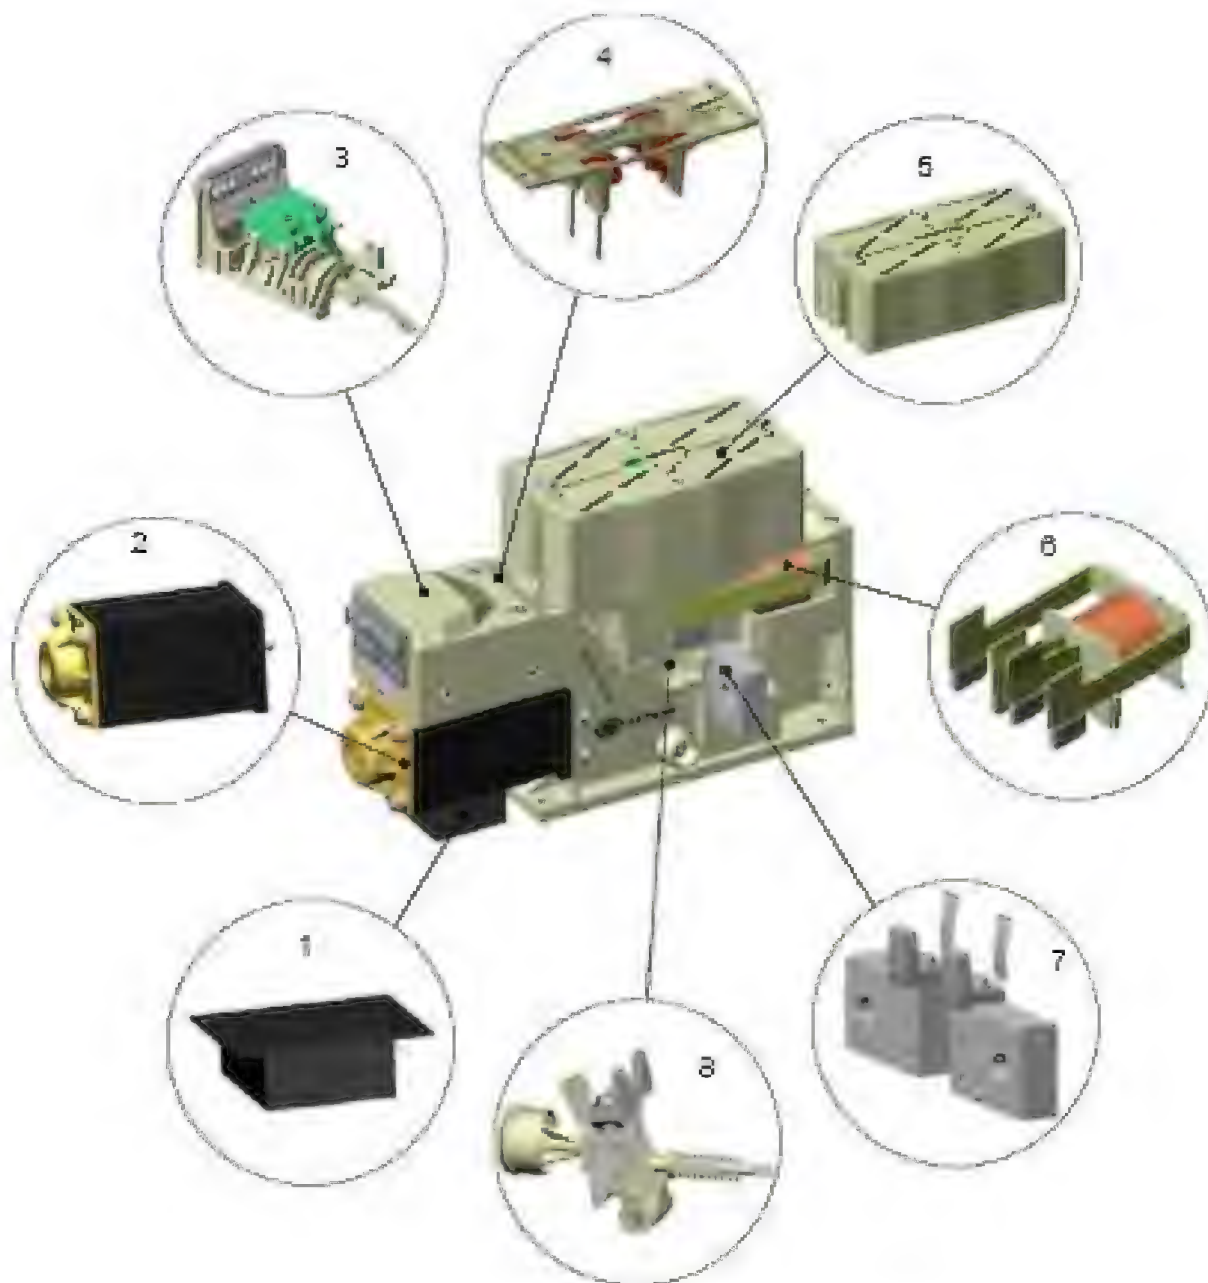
габаритный чертеж электромагнитного контактора
